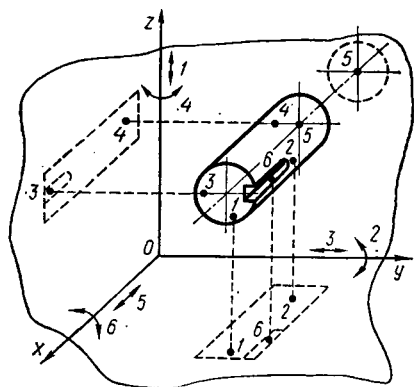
Схема базирования цилиндрической заготовки с соотношением $\frac{l}{d} \geq 1$
